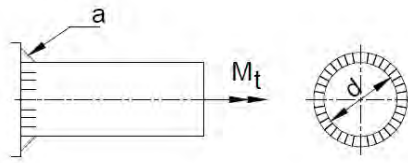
Soldadura sometida a un momento torsor
